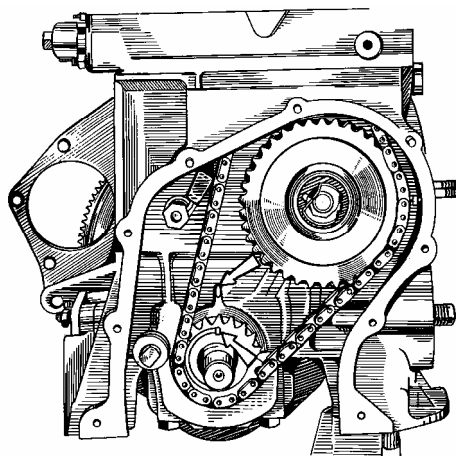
Проверка совпадения установочной метки на звездочке коленчатого вала с меткой на блоке цилиндров
